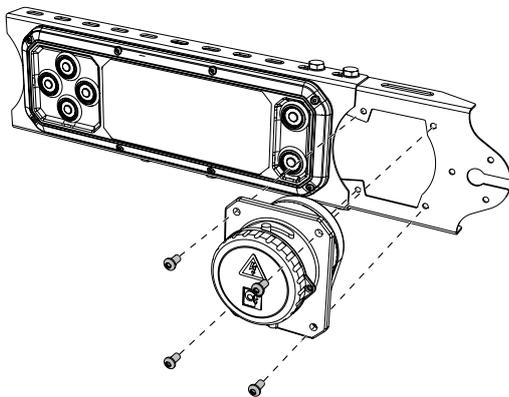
Montaje del interruptor principal junto al dispositivo de mando CD 19
